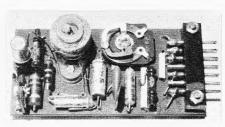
Steckeinheit des Mittelwellenaudions mit den Abmessungen 30 mm × 60 mm
